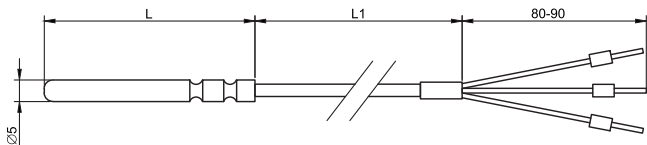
Габаритные и установочные размеры преобразователя, где:
